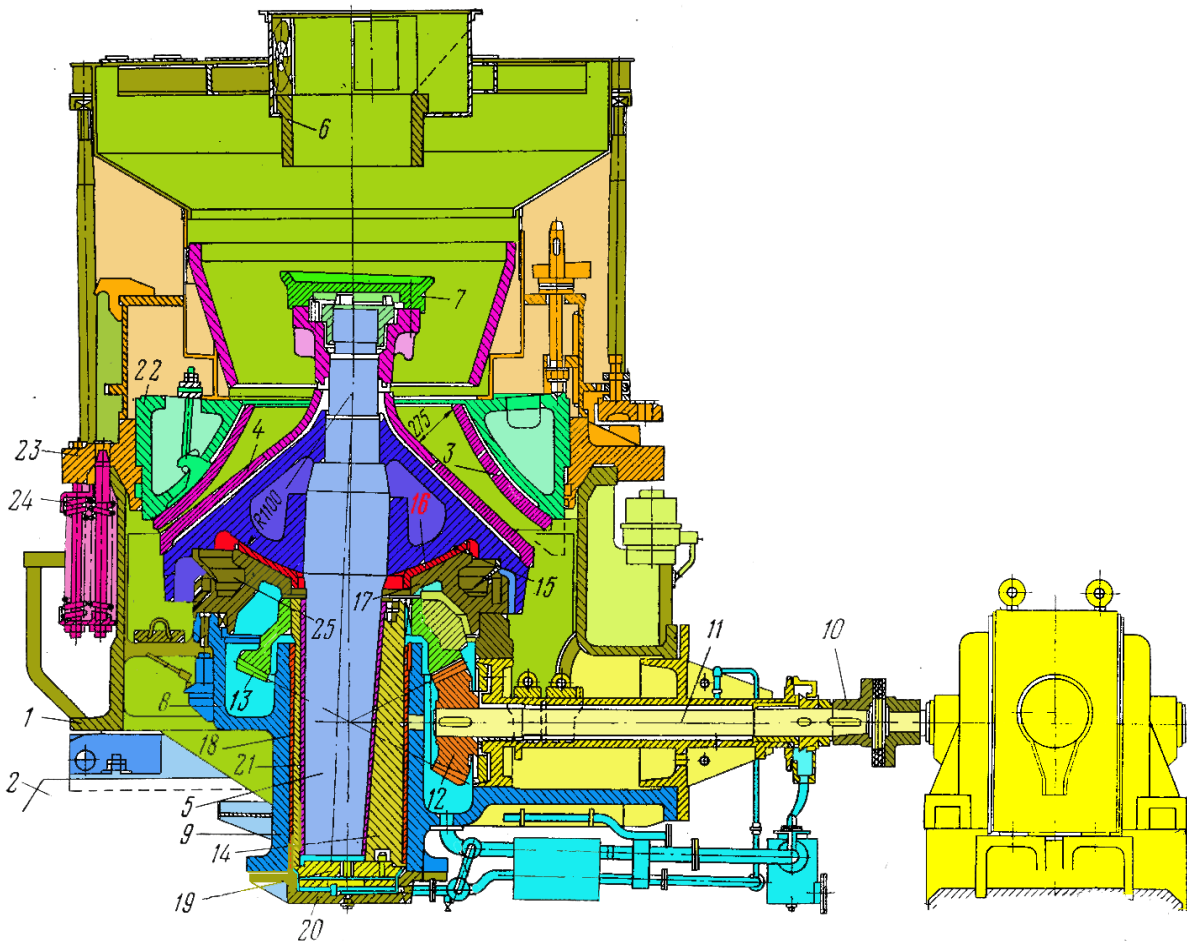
Конусные дробилки для мелкого дробления
